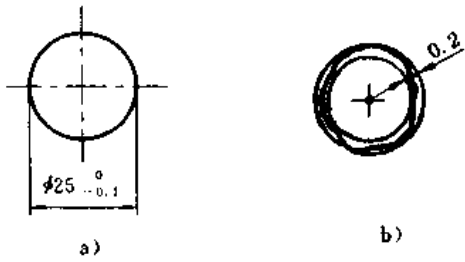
圆度未注公差值等于尺寸公差值
